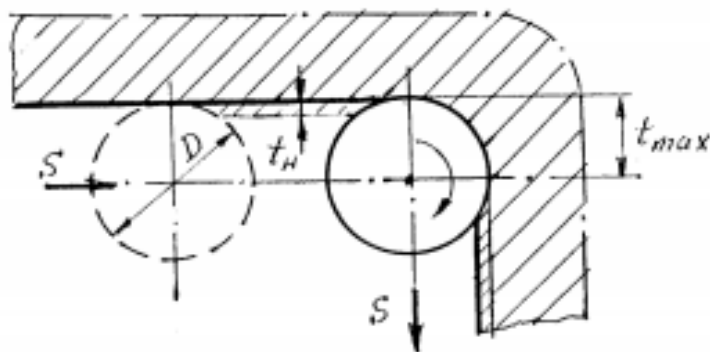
Схема обхода радиусного сопряжения концевой фрезой
